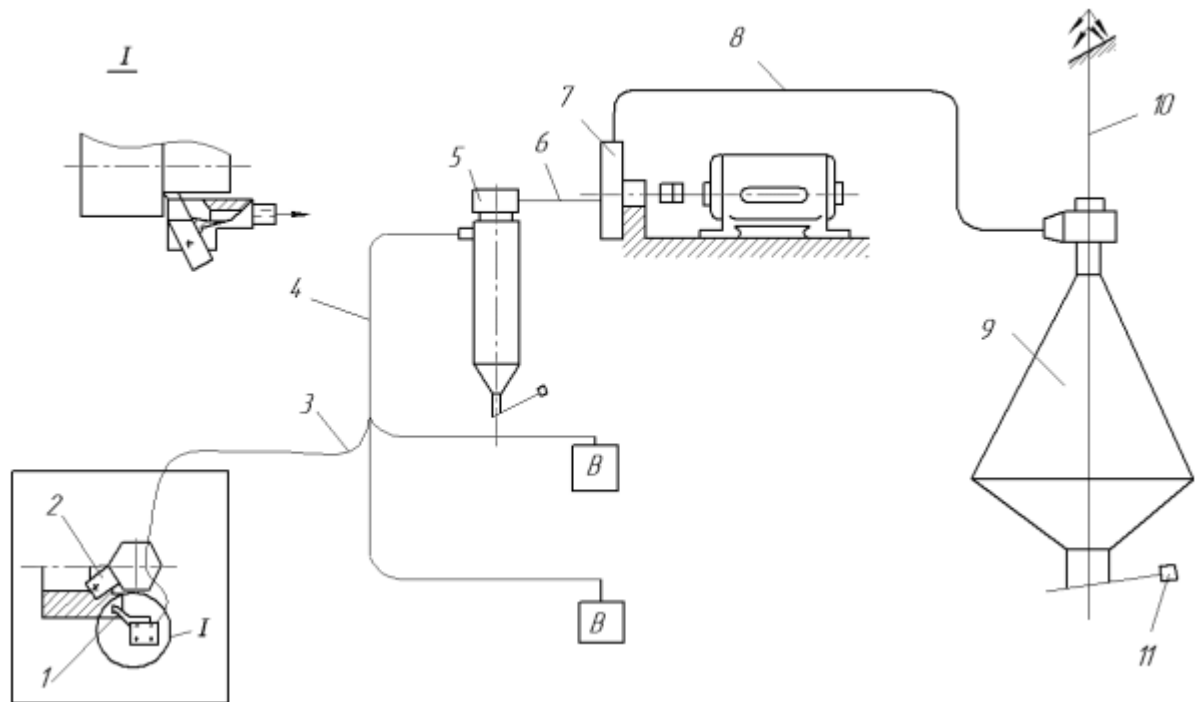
Схема групової пневмотранспортної установки для видалення стружки [6]
